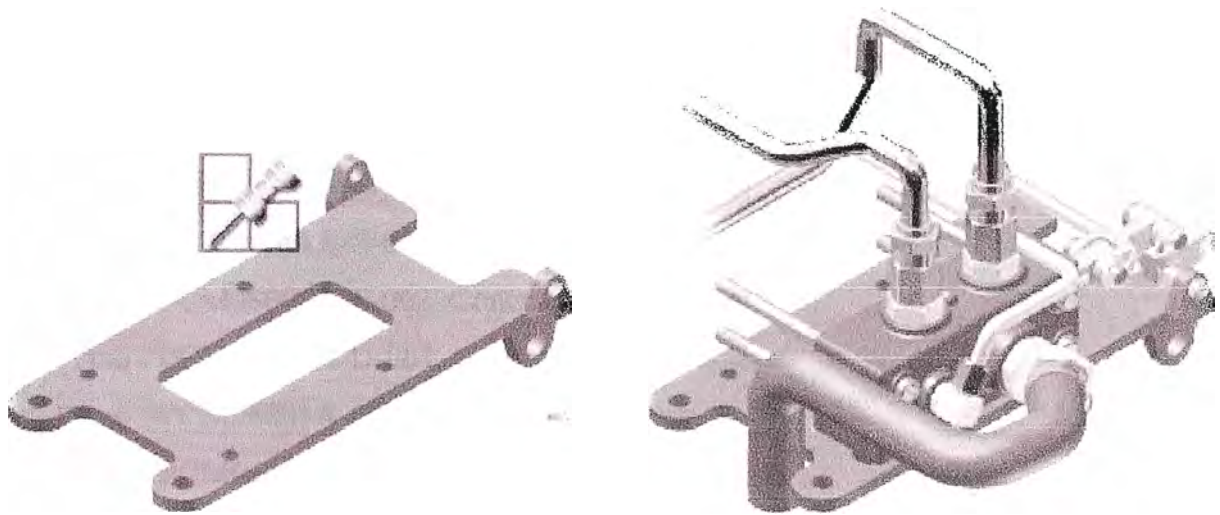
Montaje de piezas en 3D sobre base inicial
